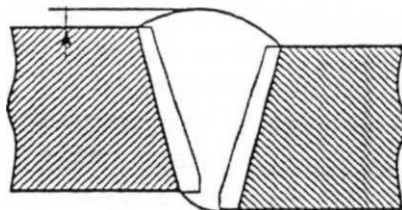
Измерение выпуклости (вогнутости) g стыкового шва при различном уровне наружных поверхностей деталей, вызванном смещением при сборке соединения под сварку
